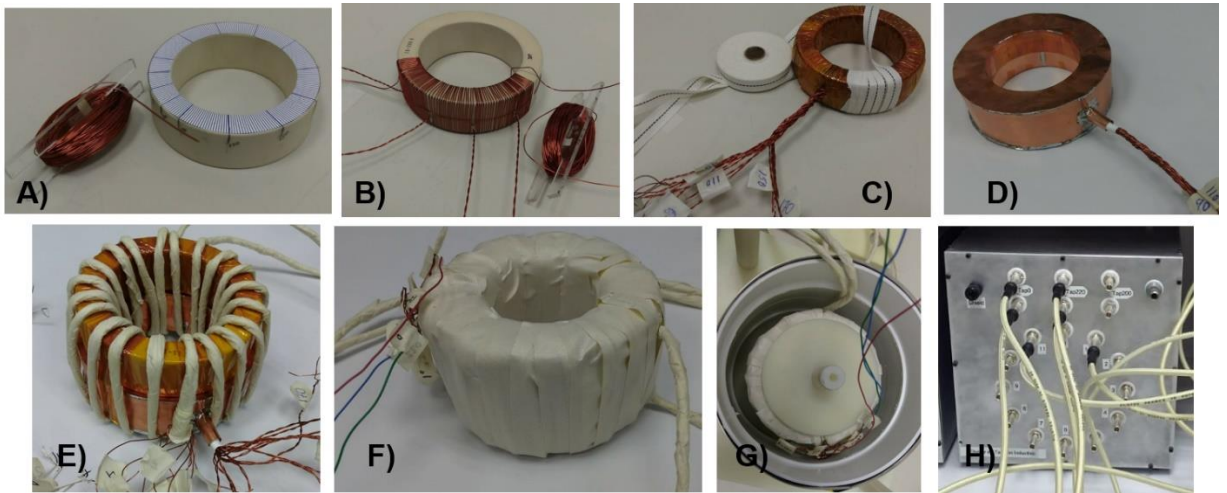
Proceso de fabricación del divisor de tensión inductivo. A) núcleo toroidal con guía para realizar el primer devanado; B) primer devanado con salidas en las vueltas 10, 30, 50, 70, 90, 110, 130, 150, 170, 190 y 210; C) aislamiento mediante cinta Kpaton y cinta de algodón; D) blindaje eléctrico mediante lámina de cobre; Segundo devanado con trenza de cables coaxiales sobre el núcleo con el primer devanado y núcleo extra.
